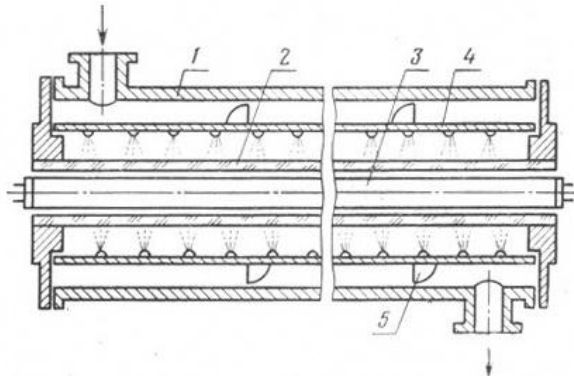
Розріз секції установки ОВУ-6П для знезаражування води УФ випромінюванням: 1 – циліндричний корпус; 2 – кварцовий чохол; 3 – дугова бактерицидна лампа; 4 – щітковий пристрій для очищення поверхні кварцової прозорої труби від водяного бруду; 5 – лопаті турбінок щіткового пристрою
